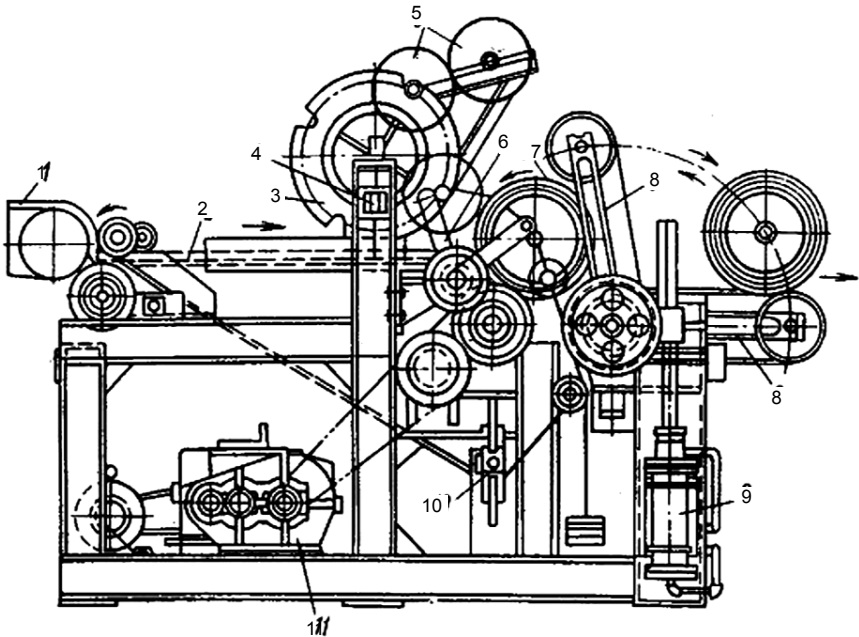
Верстат для навивання циліндрів з мінераловатного килима:
